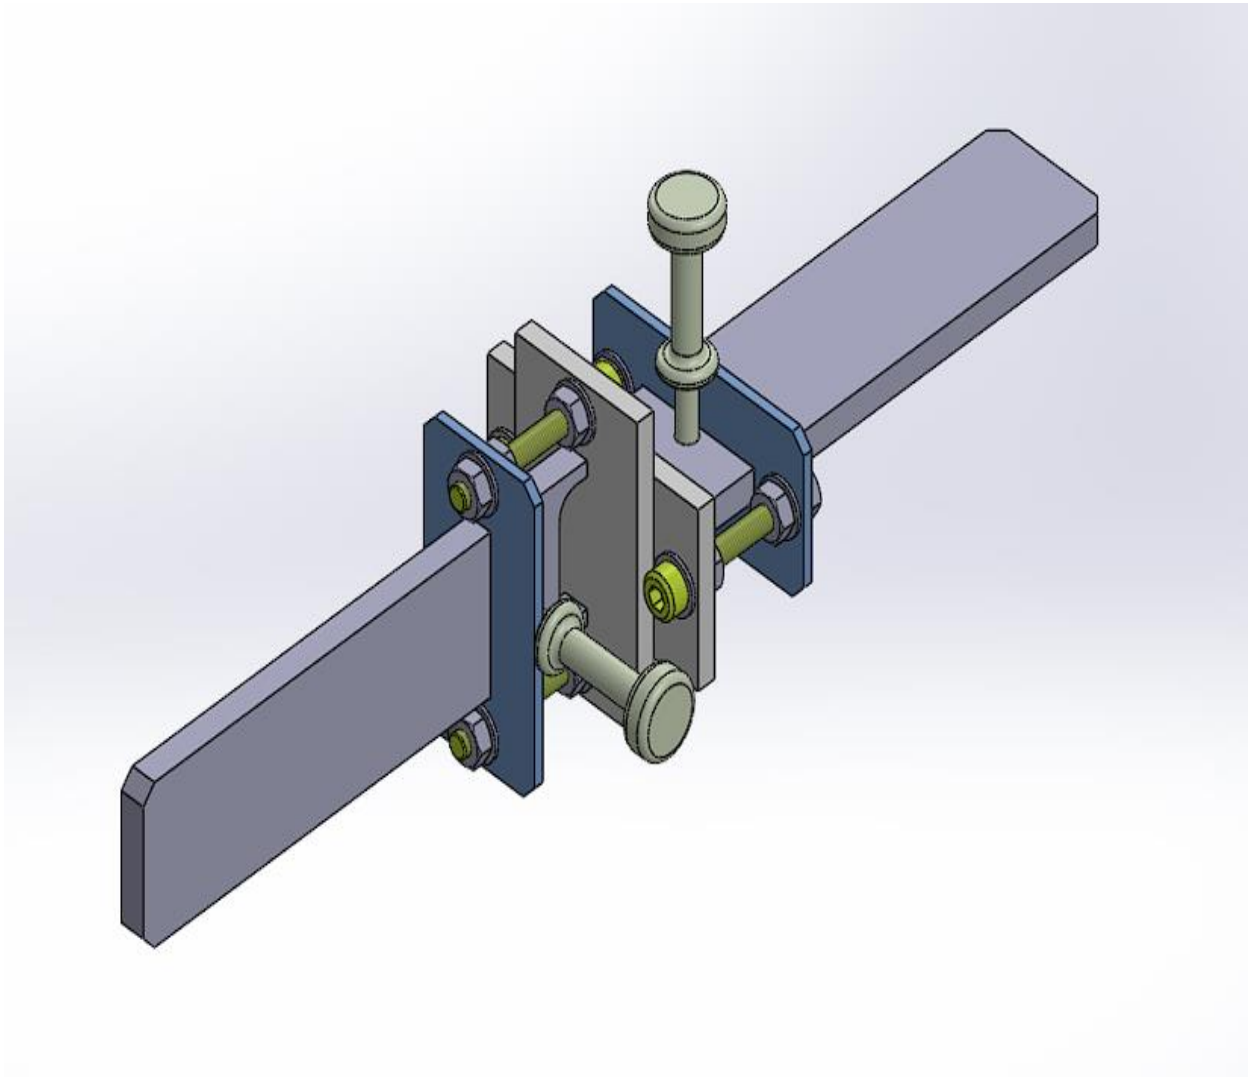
Экспериментальное приспособление для закрепления образцов
